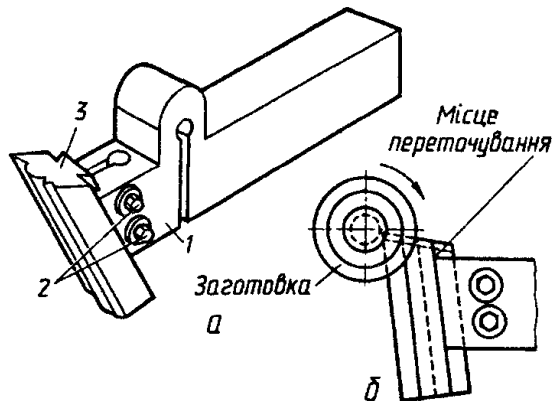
Призматичний фасонний різець: а - разом з державкою; б - схема встановлення; 1 - державка; 2 - гвинти; 3 - різець
